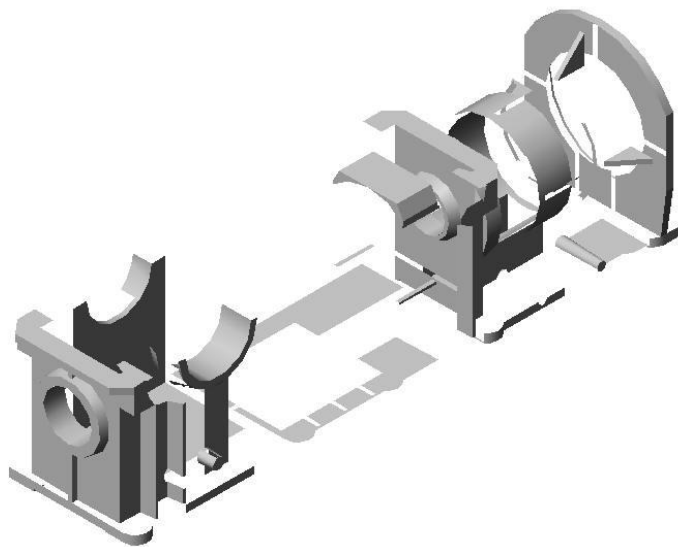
Моделирование корпуса червячного редуктора поверхностными РМЭ
